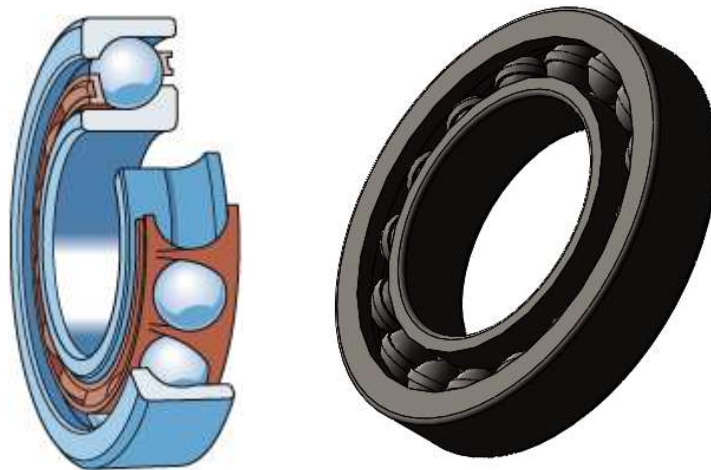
Vista de corte y 3D del rodamiento de bolas de contacto angular SKF
